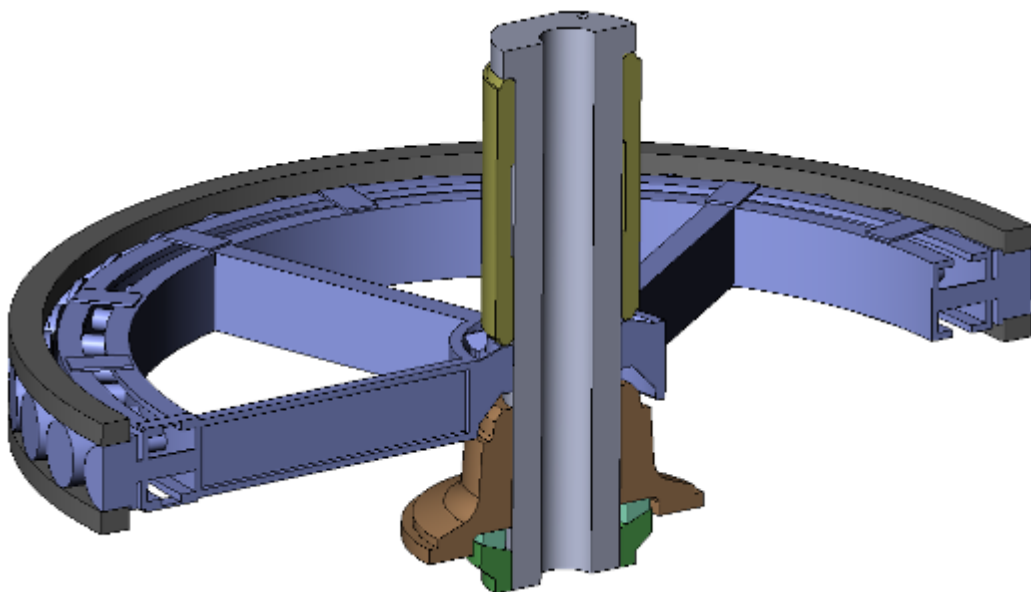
Геометрическая модель опорно-поворотного устройства экскаватора ЭКГ-10 (в разрезе)
